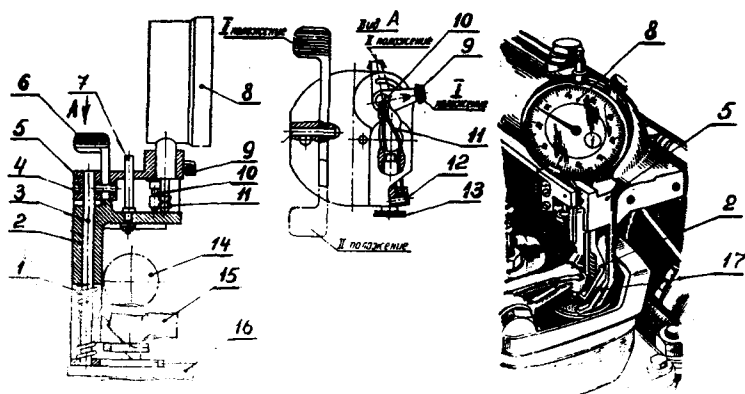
Приспособление для определения величины зазора в клапанном механизме КМ-9918
